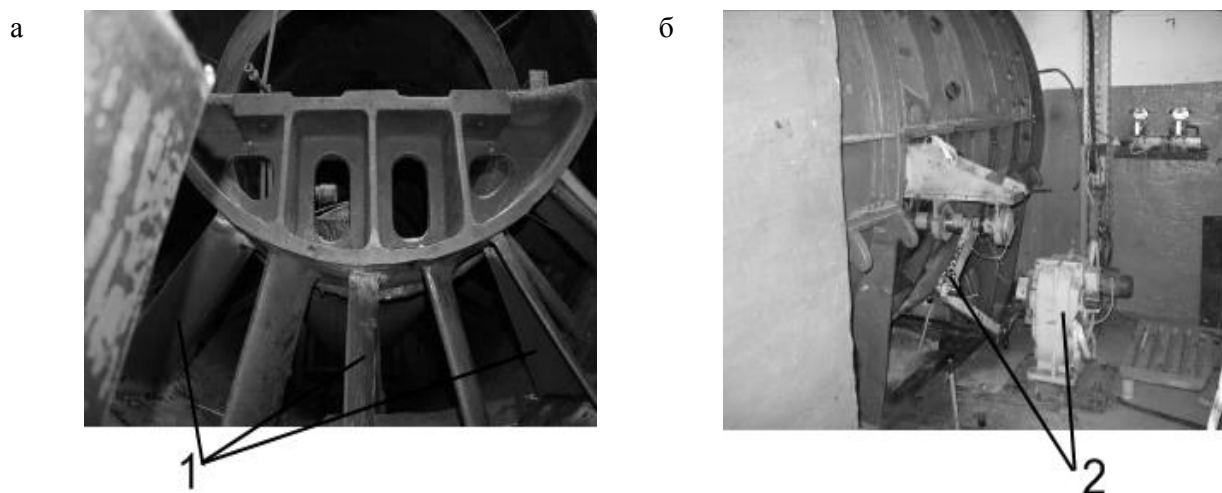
Усиление опорного блока вентилятора (а): 1 - ввариваемые листовые лопатки, однооборотный привод поворота лопаток на ходу рабочего колеса вентилятора (б); 2 - установка однооборотного механизма
